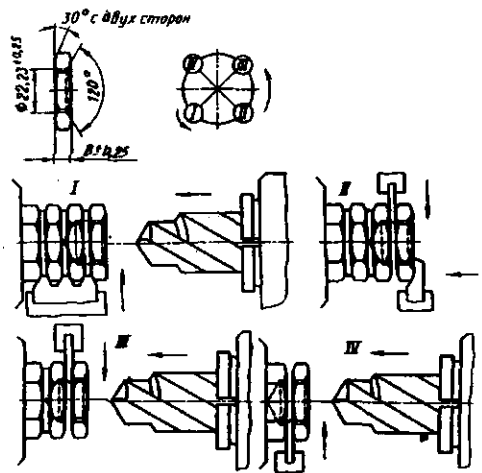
Наладка четырехшпиндельного автомата для обработки гаек одинакового размера
